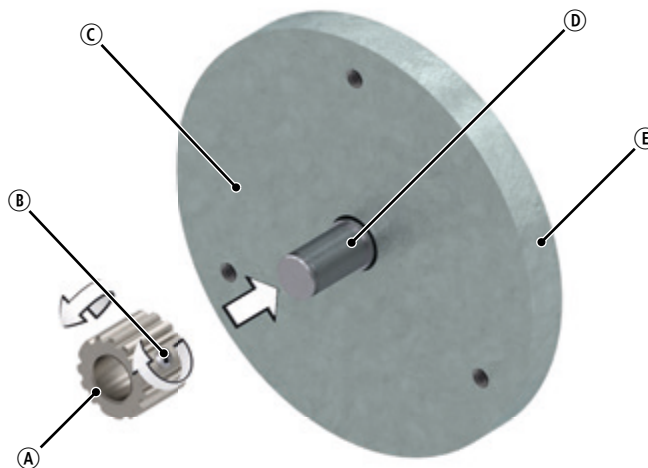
Montage der Nabe mit Madenschrauben (für Baugrößen 01 und 02)
